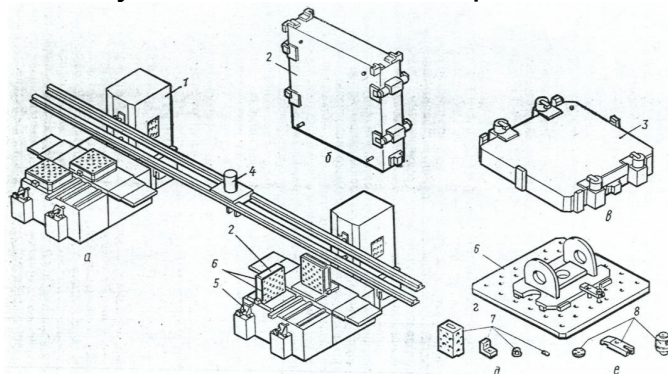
Участок ГПС, оснащенный обратимой технологической оснасткой: а – общий вид участка; б - базовое вертикальное приспособление; в – базовое горизонтальное приспособление; г – плата-спутник; д – установочные и опорные элементы; е – зажимные элементы
